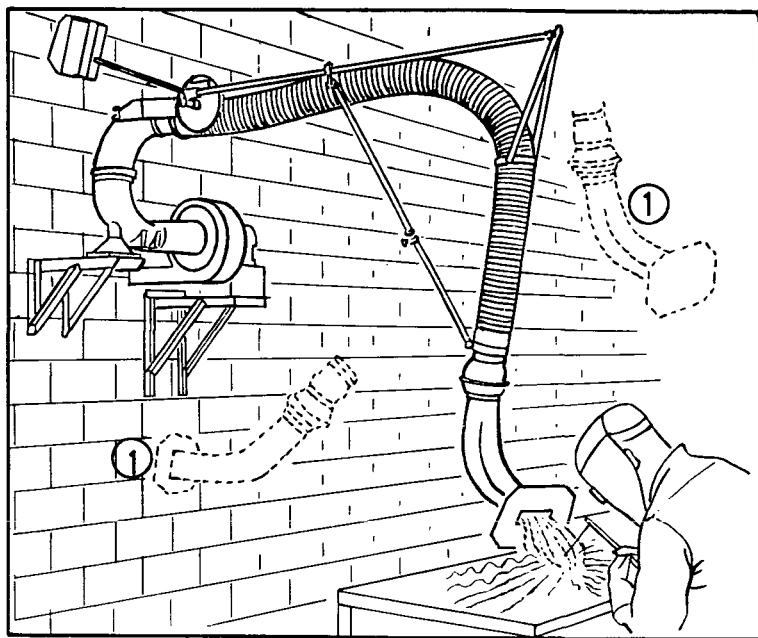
Aspiración de los humos que se producen en las operaciones de soldadura por arco eléctrico por medio de una boca de aspiración móvil.
